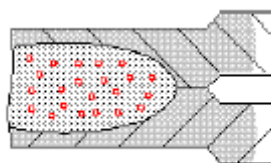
Representação de porosidade no ponto de soldadura
